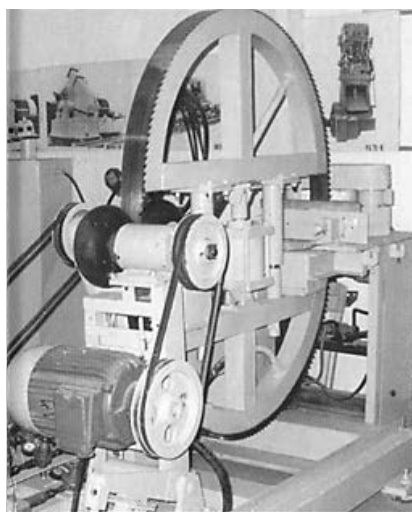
Общий вид ленточнопильного станка с пилой, движущейся по криволинейным аэростатическим направляющим
